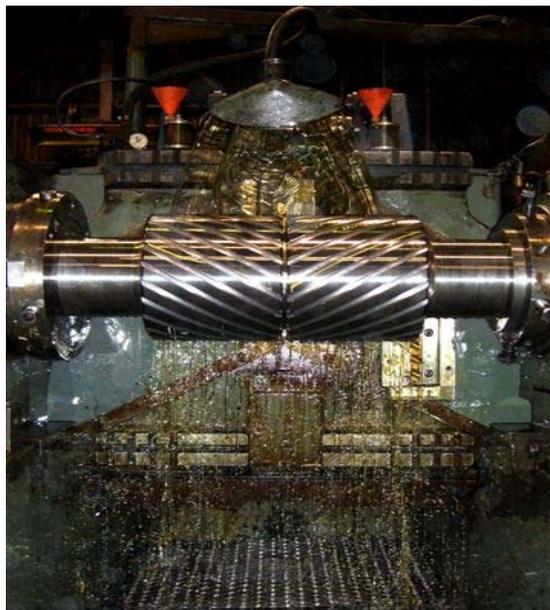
Обработка шевронной вал-шестерни обкаточными резцами
